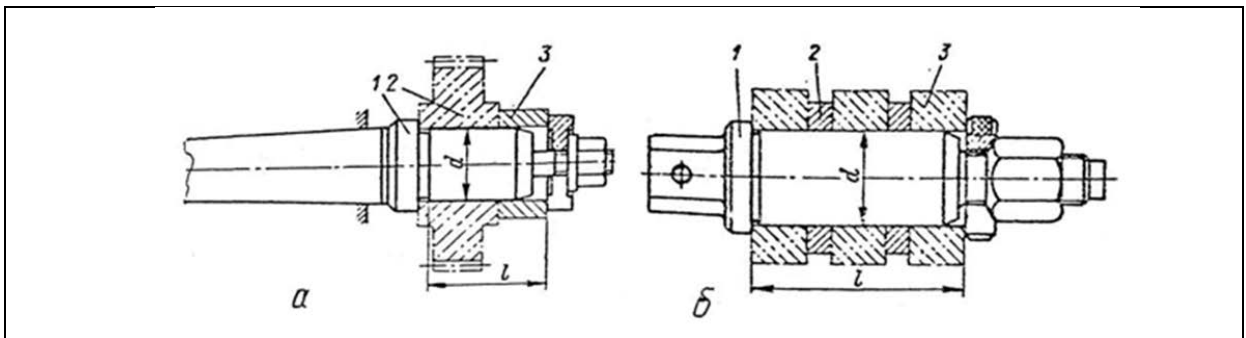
Установлення заготовок на жорсткі циліндричні оправки: а, б – із гарантованим зазором
